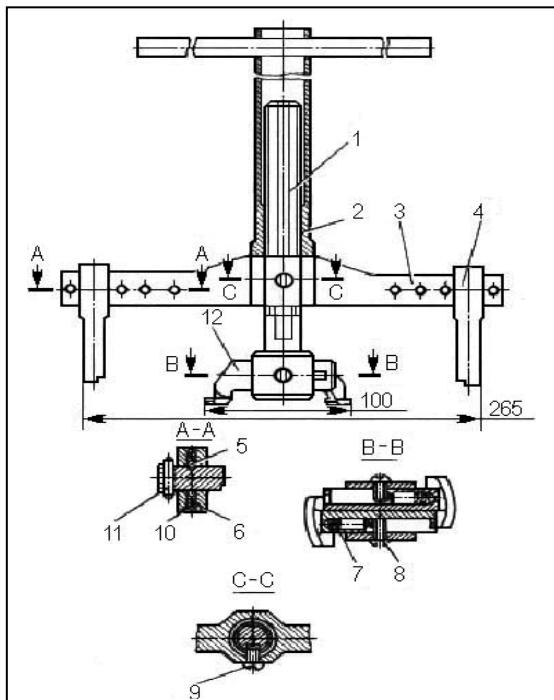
Съемник для выпрессовки наружных колец подшипника из картера, крышек ведущей конической шестерни и ступиц колес:
